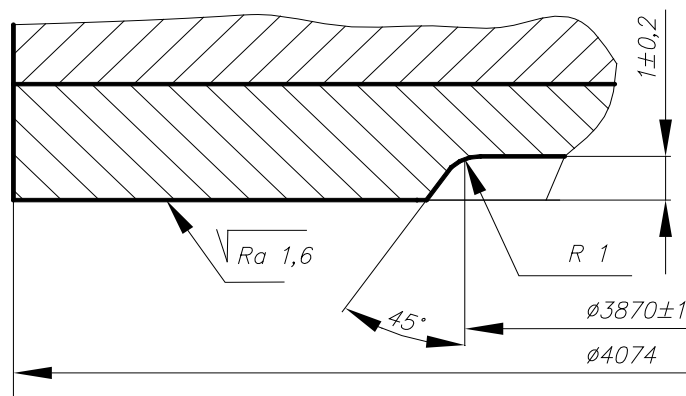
Ущільнююча поверхня кришки реактора
